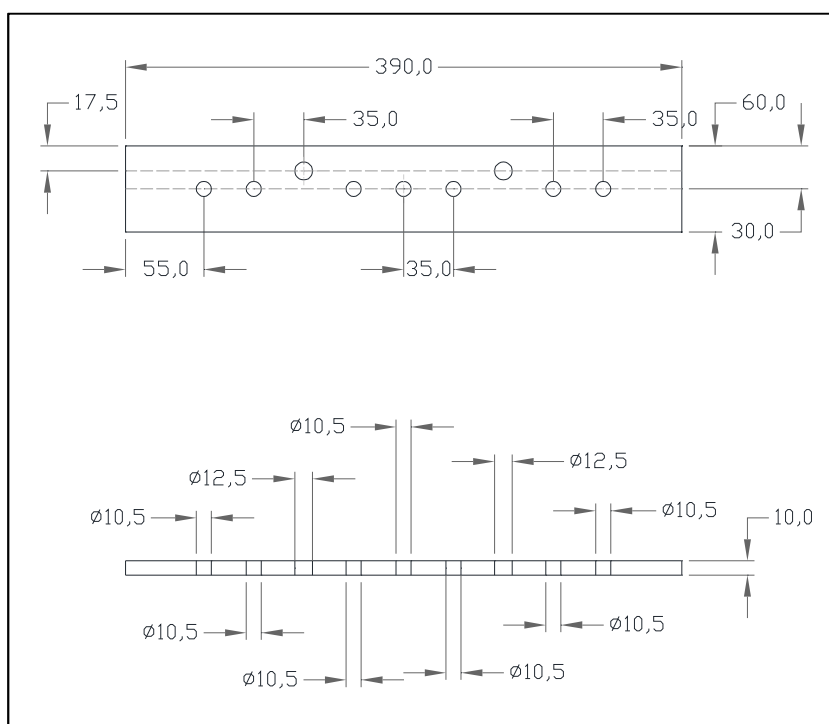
Barra de terra (plana) para caixa de inspeção pré-fabricada do tipo F
